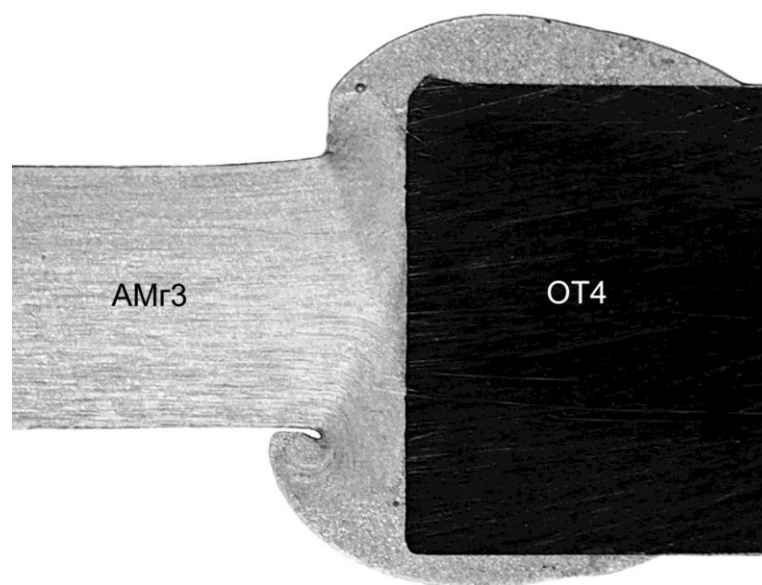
Макроструктура сварного соединения ($\times 4$)
